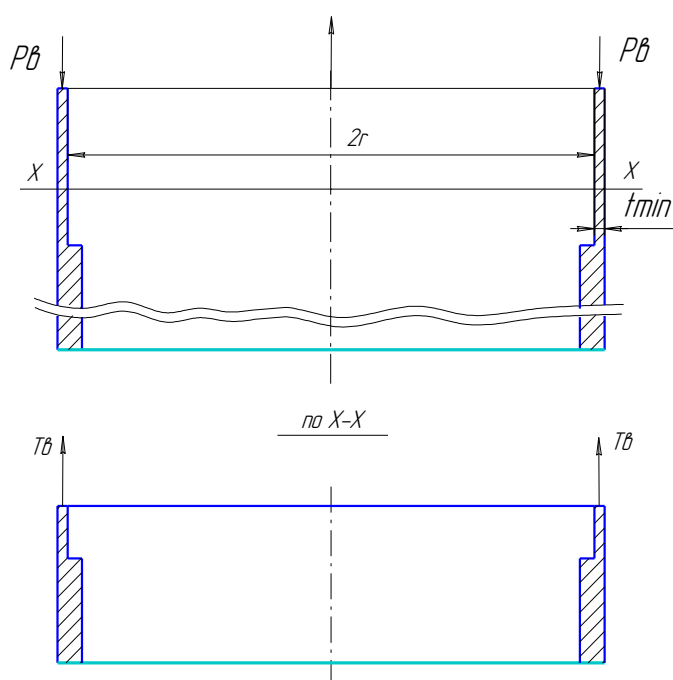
Расчет устойчивости стенки от вертикальных (осевых) нагрузок
